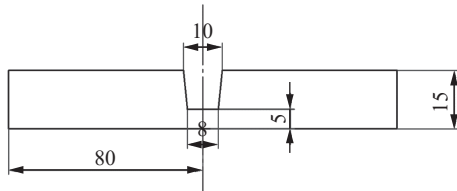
焊接试样坡口尺寸示意图 (mm)
